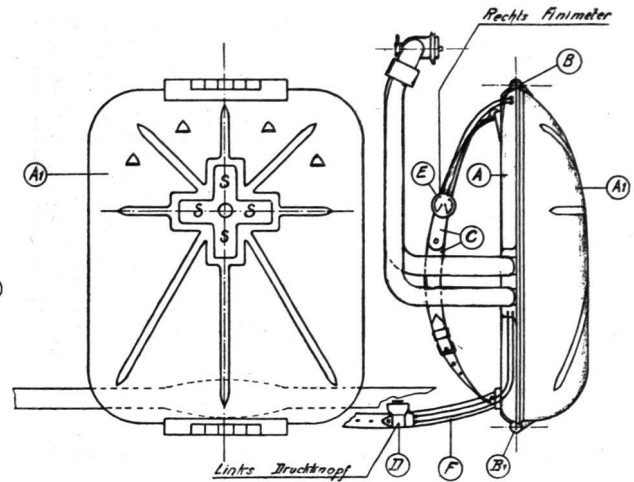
SOS-Gerät - Rückansicht, Seitenansicht
